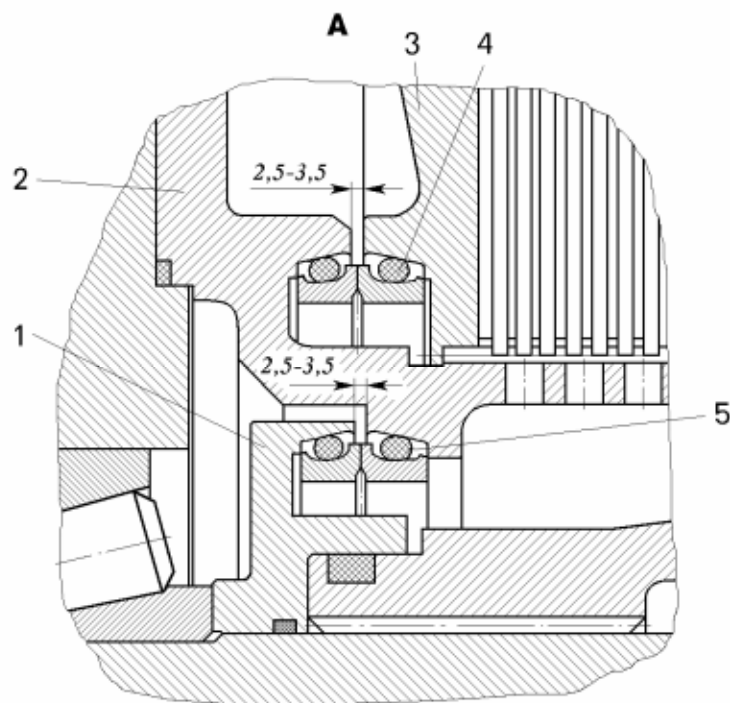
Установка торцовых уплотнений в тормозном механизме задних колес (вид А смотри рисунок 11.29):
